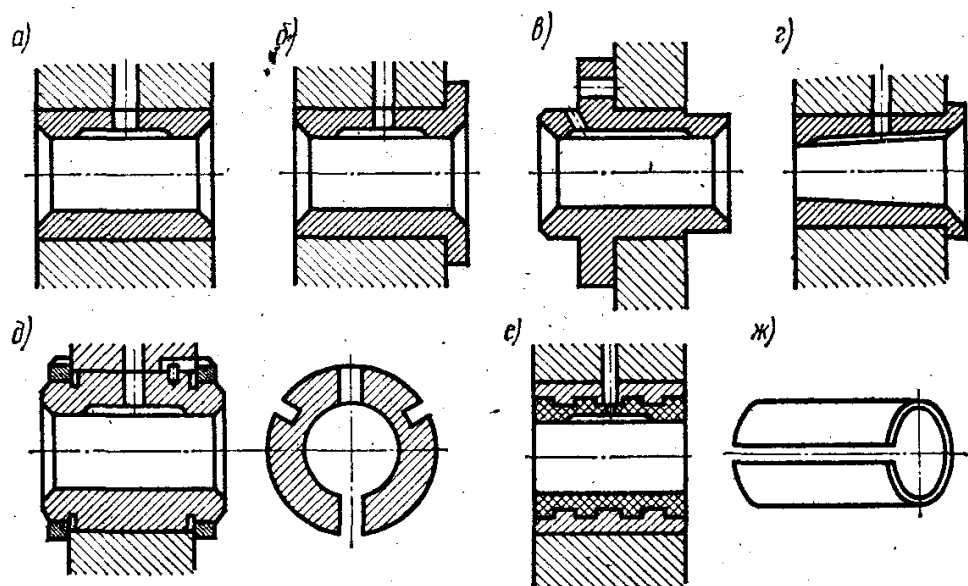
Конструктивные разновидности подшипниковых втулок
